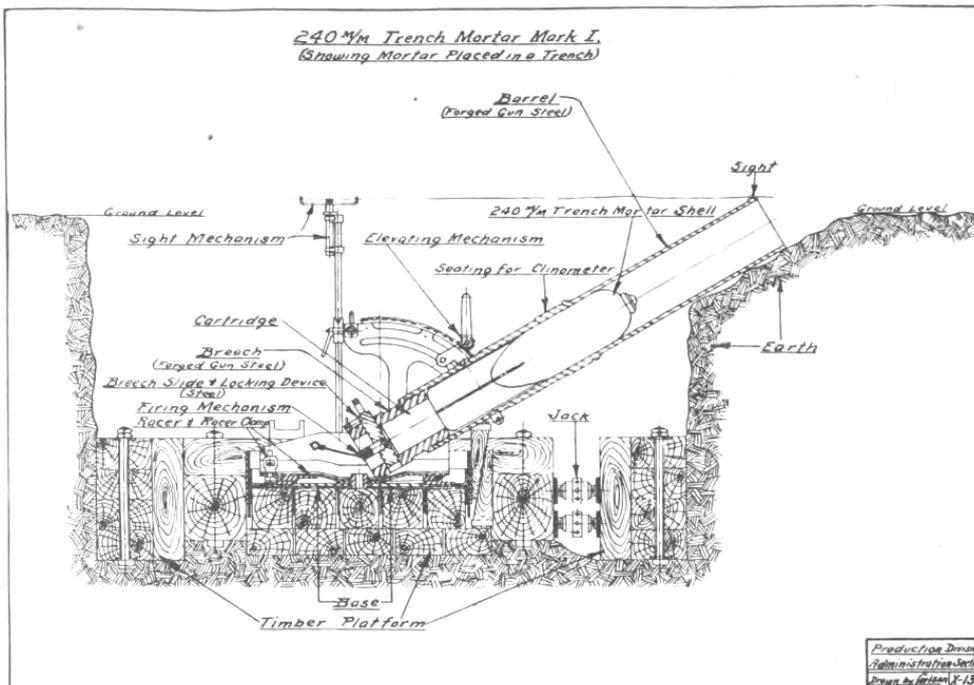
9,45 inch (240 mm) Heavy Mortar, Schnitt mit Stellung,
